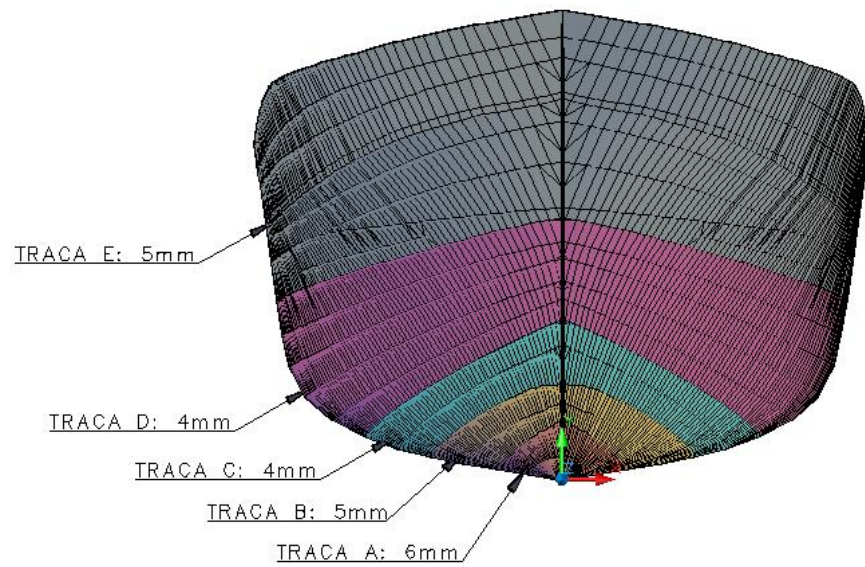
g: *Generación de planchaje de fondo y costado
